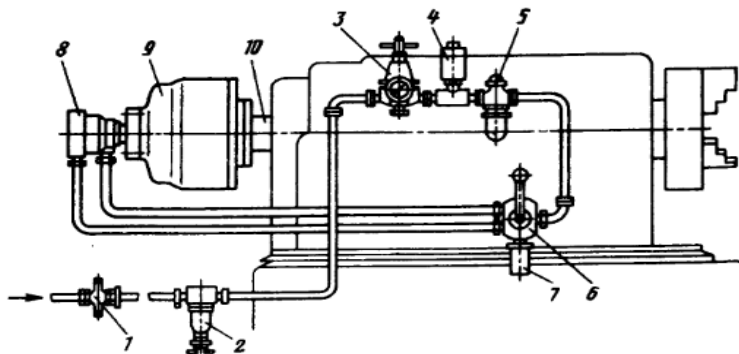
Схема пневмопривода к приспособлению токарного станка.
